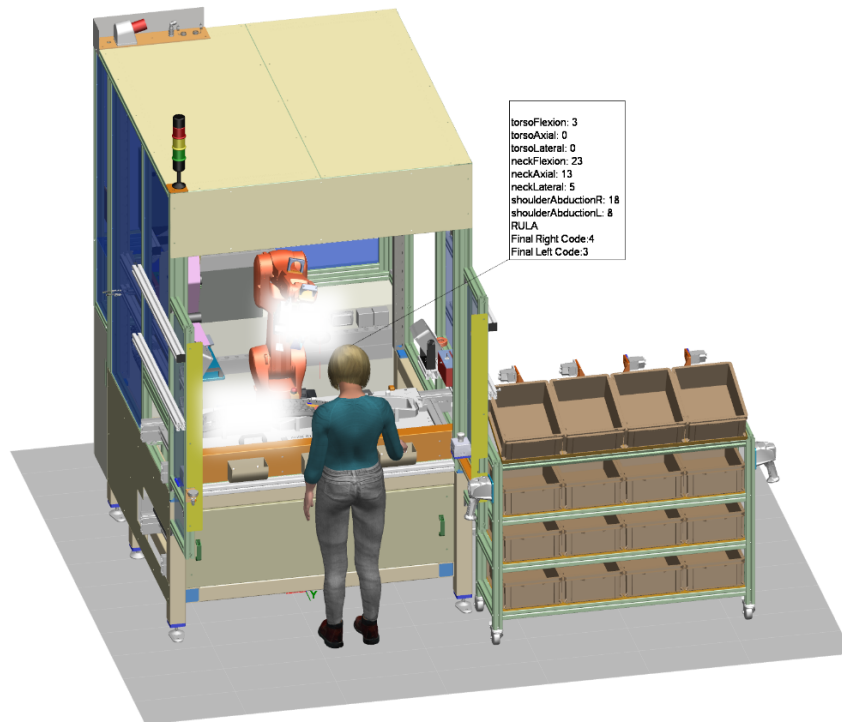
Nové řešení odebírání kabelů ze zásobníku
